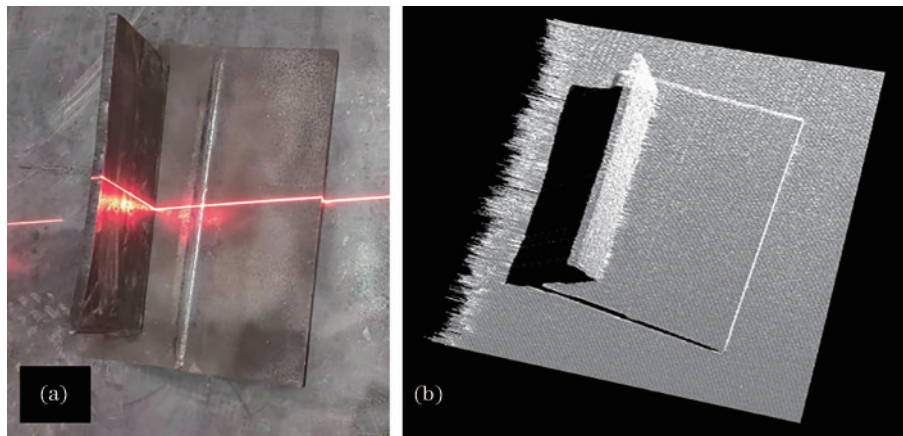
焊接工件 3D 重构。(a)金属工件;(b) 3D 点云
